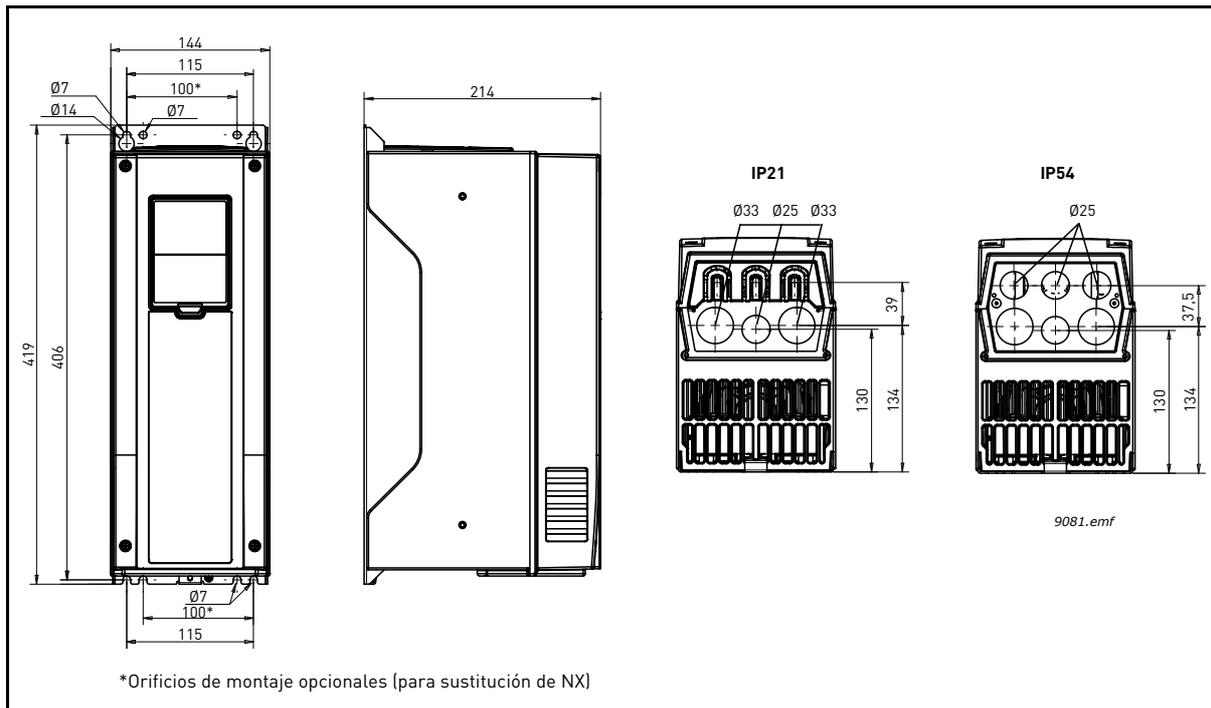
Dimensiones del variador de CA Vacon, MR5, montaje para la pared
